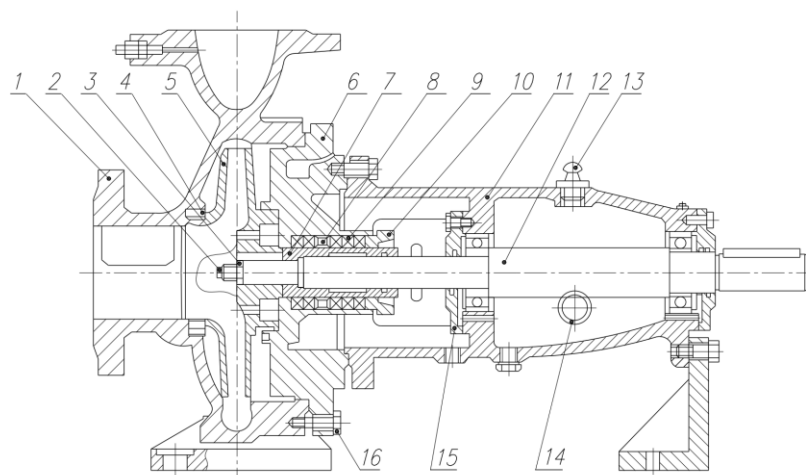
Схема конструкції консольного насоса 1 – корпус; 2 – гайка робочого колеса; 3 – стопорна шайба; 4 – ущільнення корпусу; 5 – робоче колесо; 6 – кришка корпусу з корпусом ущільнення; 7 – захисна втулка; 8 – кільце сальника; 9 – сальникова набивка; 10 – кришка сальника; 11 – корпус
